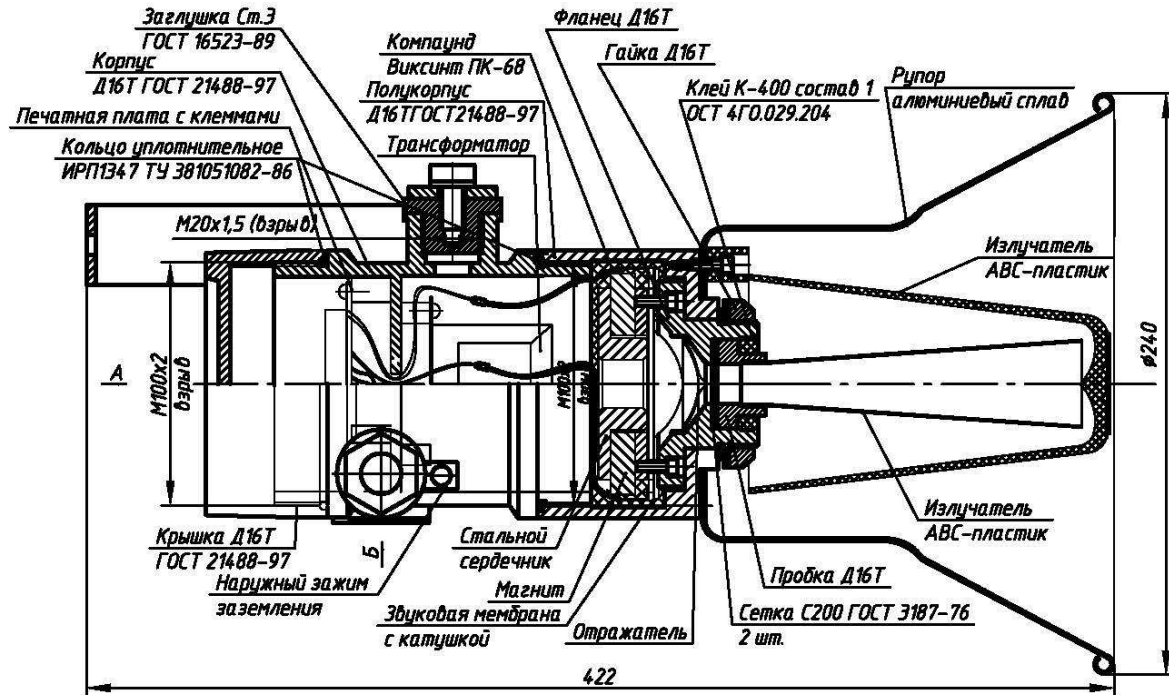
Габаритный чертёж речевого блока Оповещателя СПИКЕР, совмещённый с чертежом средств взрывозащиты.
